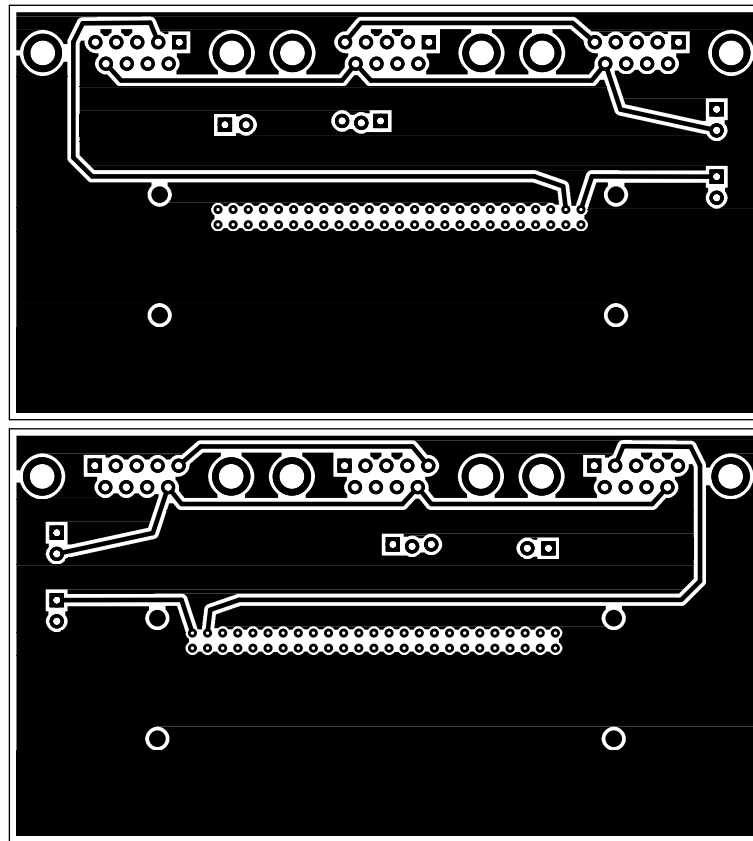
Circuito impresso da placa *Sensor Shield* em tamanho real. Parte superior.
